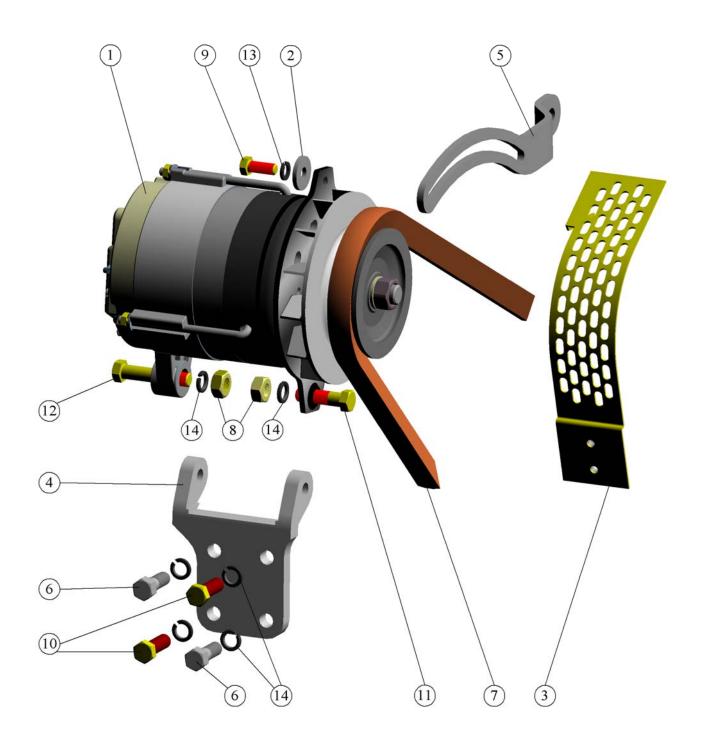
Установка генератора. Fig. 23 Generator installation.
